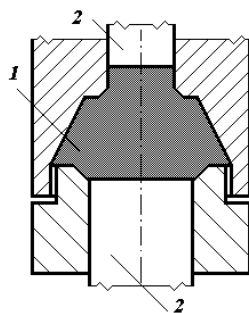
Закрытая штамповка: 1 - поковка; 2 – выталкиватели
